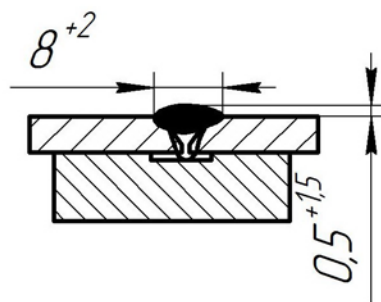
Эскиз конструктивных элементов продольного сварного шва обечайки после сварки второго прохода
